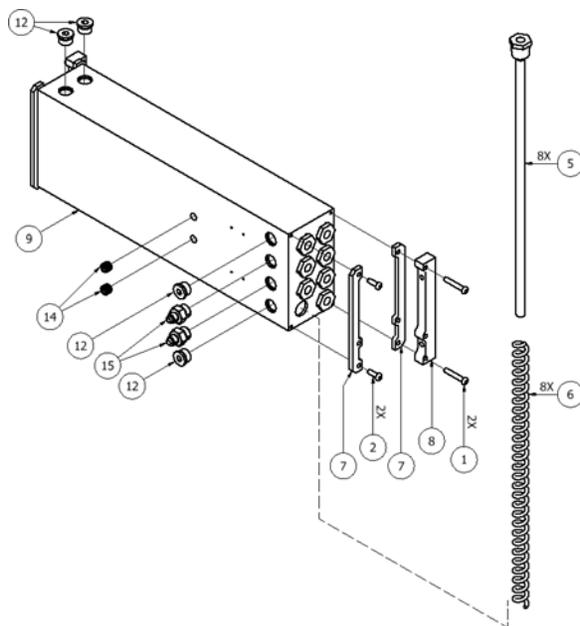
Ensamblaje del calentador, 8 varillas - A
